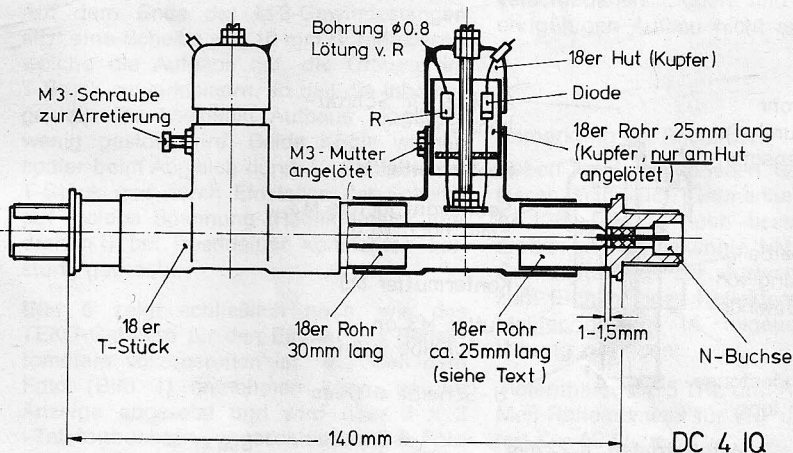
Prinzipieller Aufbau mit den Hauptabmessungen
